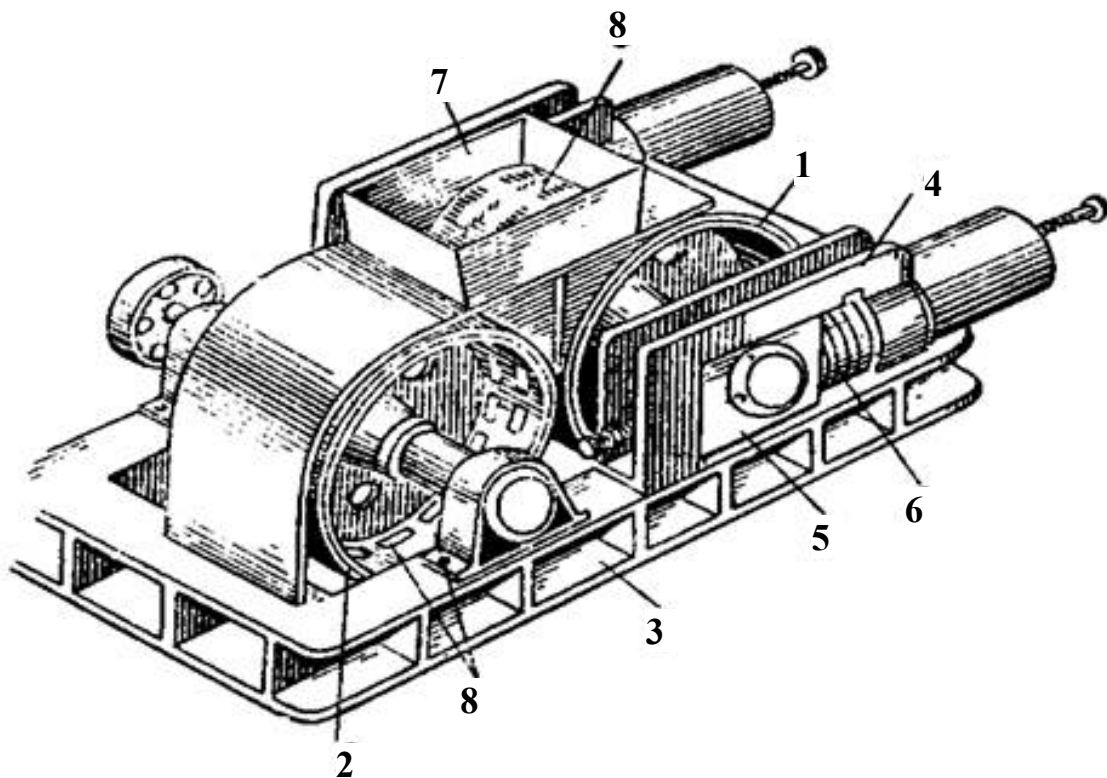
Вальці дірчасті: 1 – тихохідний валок; 2 – швидкохідний валок; 3 – рама; 4 – напрямні; 5 – рухомий підшипник; 6 – пружина; 7 – приймальна воронка; 8 – отвори
